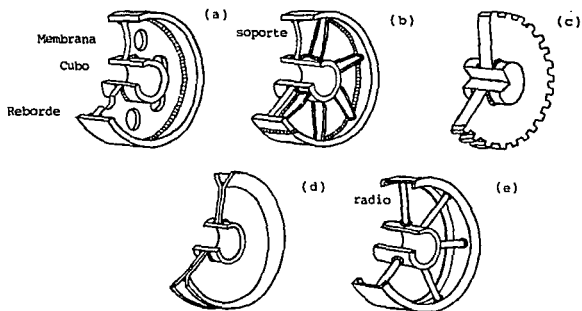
Tipos de ruedas soldadas.
